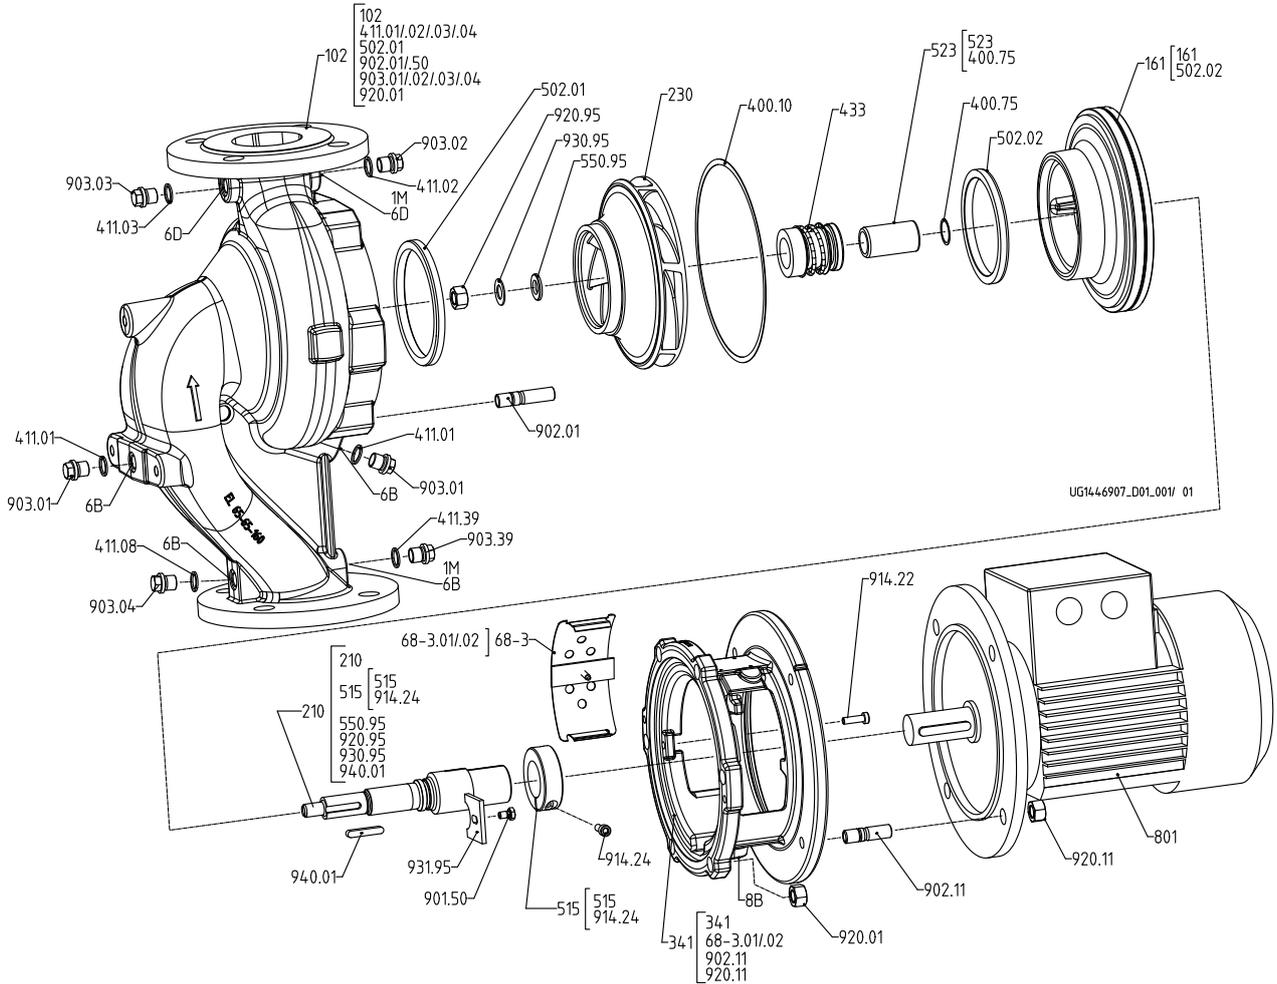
Ausführung mit Einzelgleitringdichtung und geklemmtem Gehäusedeckel
